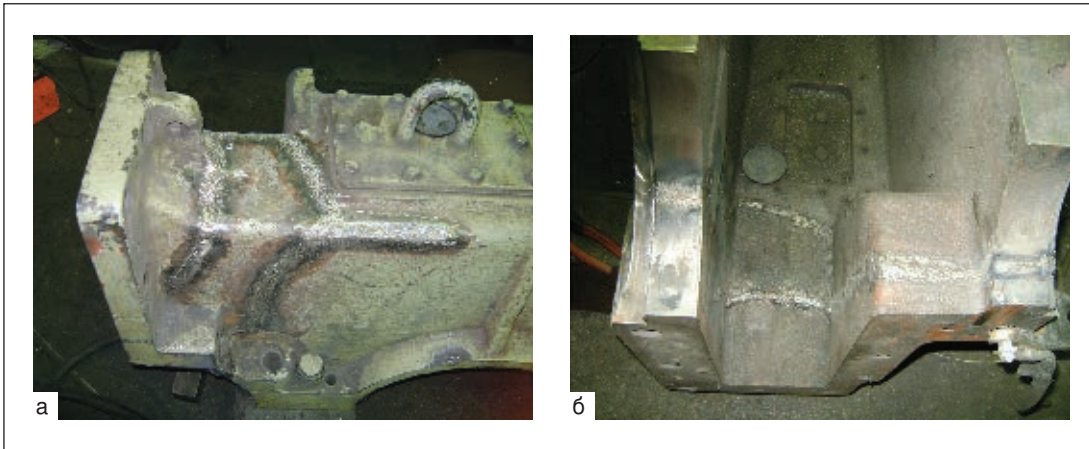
Общий вид крышки после ремонта: а — снаружи; б — изнутри
